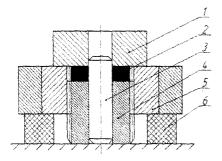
Схема штампа для деформации заготовки сложного профиля: 1 – незаходящий пуансон; 2 - заготовка, полученная в штампе; 3 – игла; 4 – нижний пуансон; 5 – матрица; 6 - демпфер
